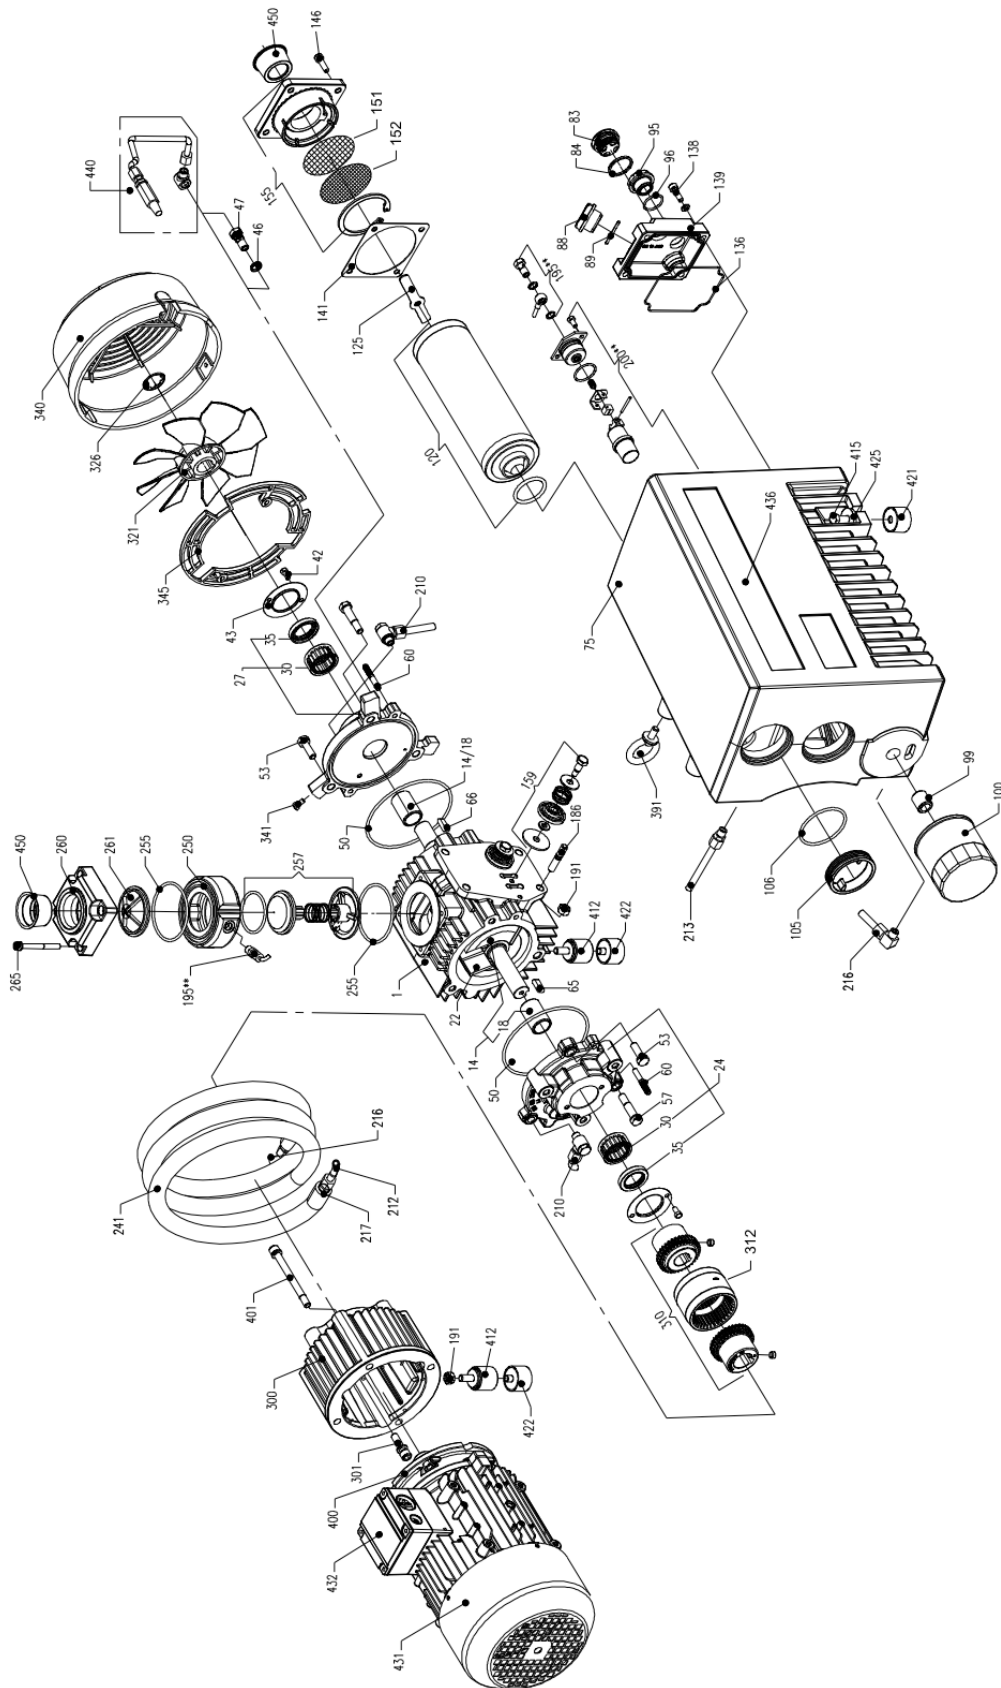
Explosionszeichnung der Modelle -0063 / -0100
